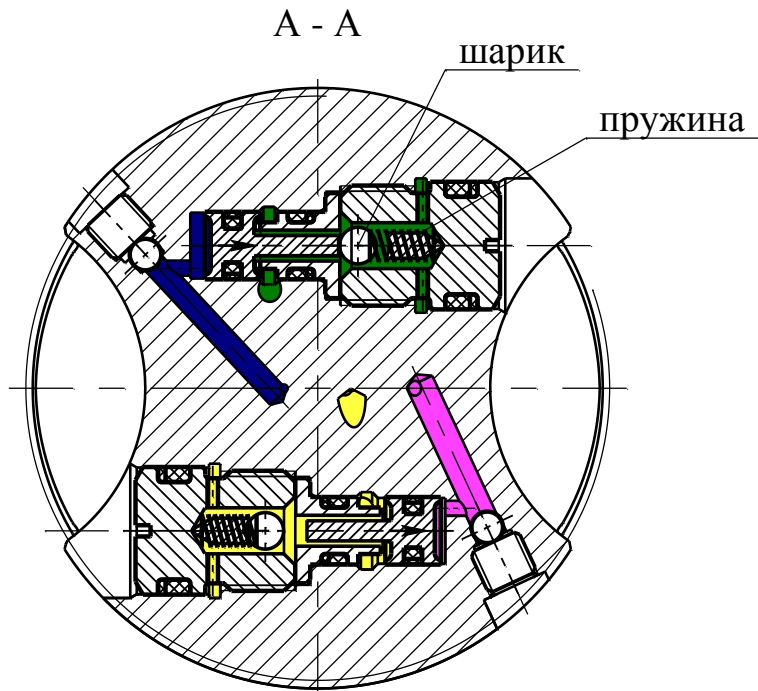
Эскиз корпуса гидрозамка для разведения ножей
